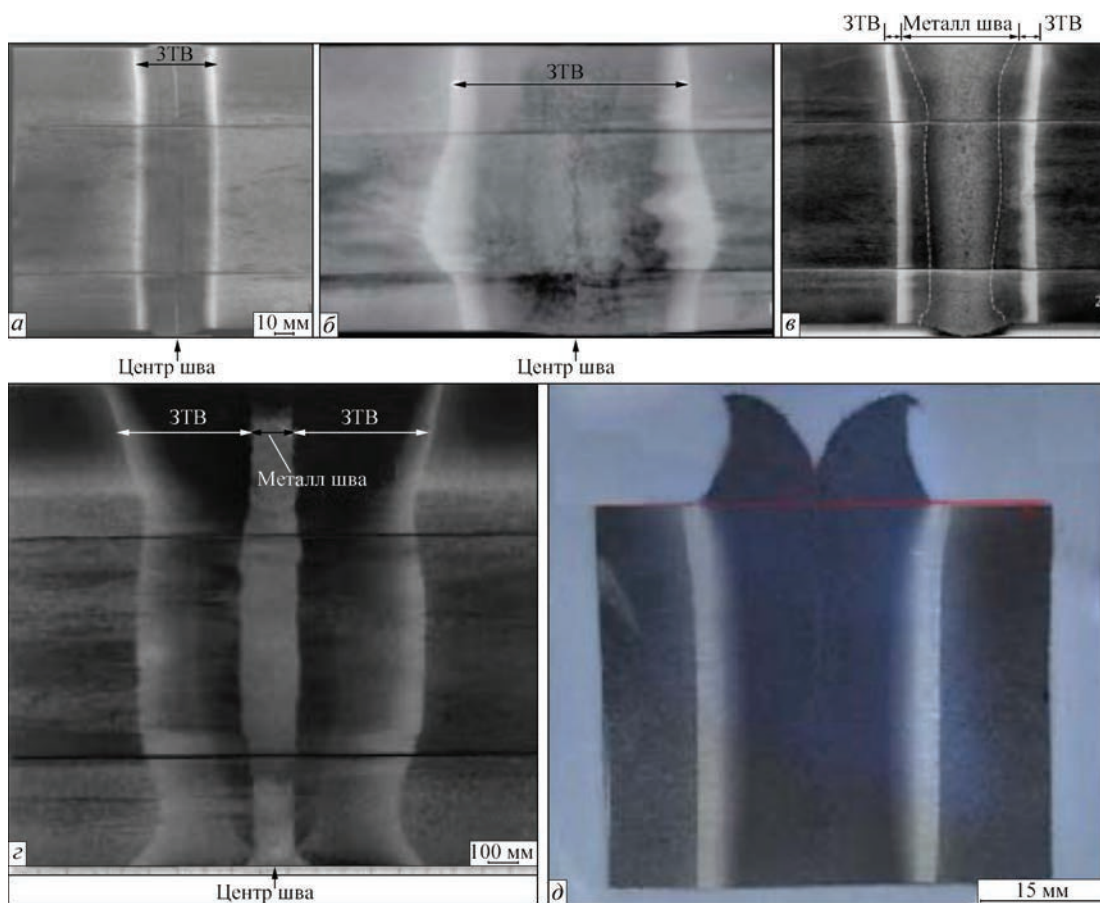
Макроструктуры сварного стыка рельса, сваренного разными способами [17]: *a* — контактно-стыковая сварка оплавлением; *б* — газопрессовая сварка; *в* — алюминотермитная сварка; *г* — сварка закрытой дугой (Enclosed arc welding); *д* — линейная сварка трением
